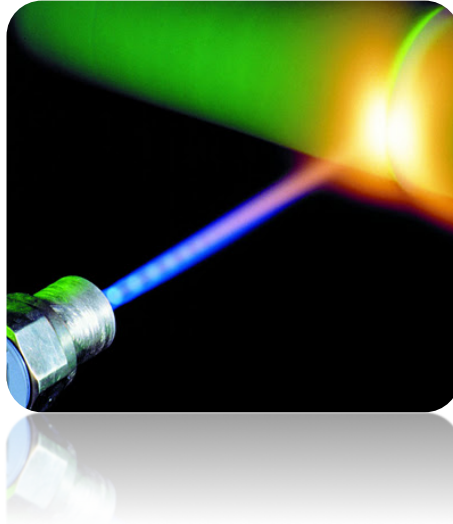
Exemple tipus de làser per la soldadura.
